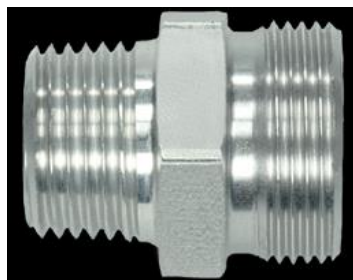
Загальний вигляд метричної конічної різі – ліва частина деталі
